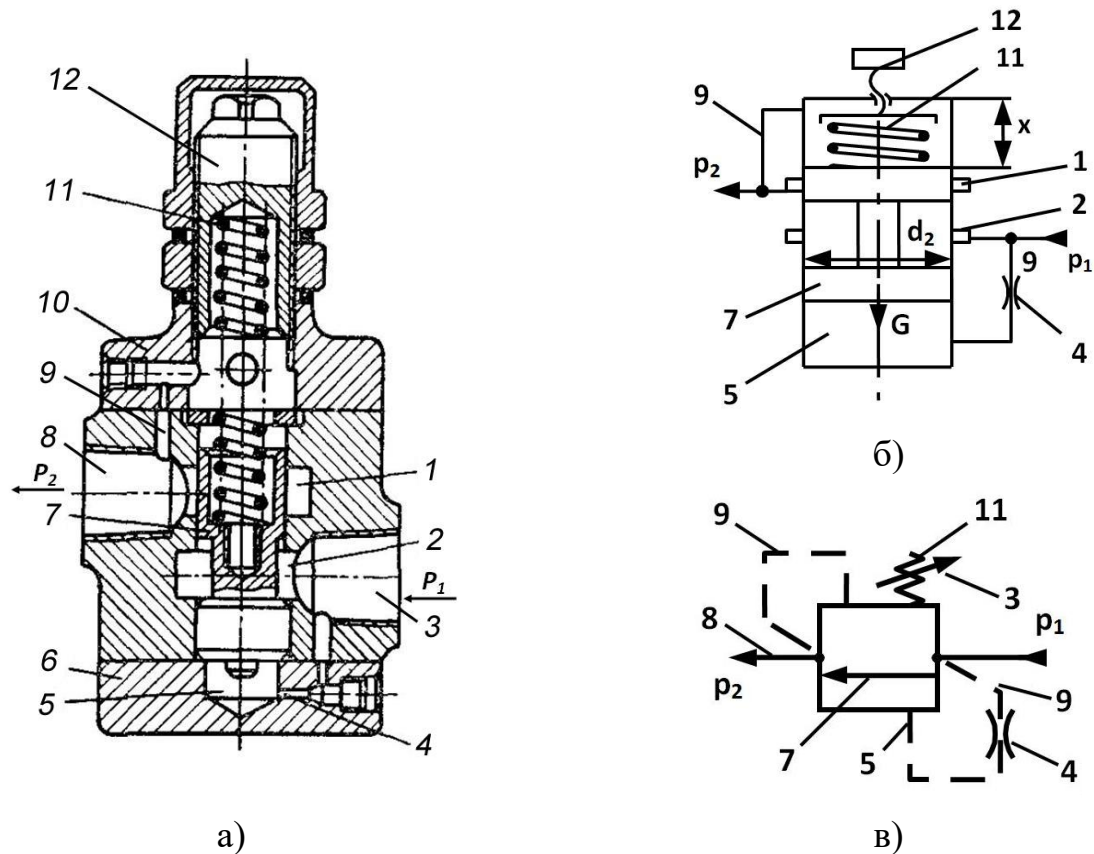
Напорный золотник: а) конструктивная схема; б) расчетная схема; в) условное обозначение; 1,2 – полости подвода и отвода; 3, 8 – присоединительные отверстия; 4, – дроссель; 5 – управляющая полость; 6,10 – крышка; 7 – плунжер; 9 – корпус; 10 – корпус; 11 – пружина; 12 – регулировочный винт.
